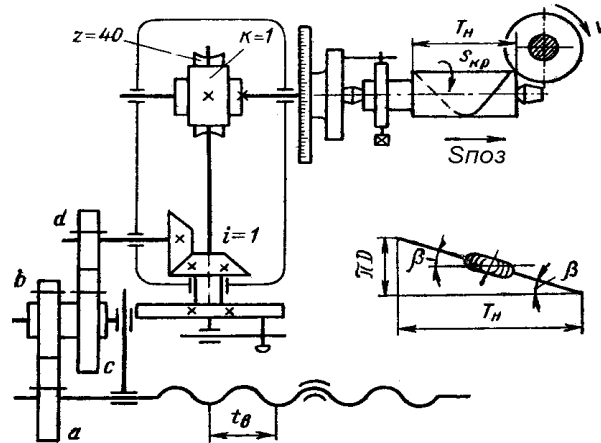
Схема налагодження ділильної головки на фрезерування спіральних канавок
